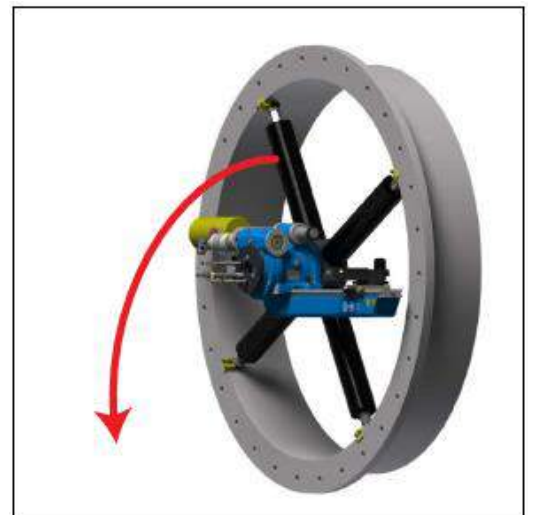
Fallgefahr bei senkrechter Installation
